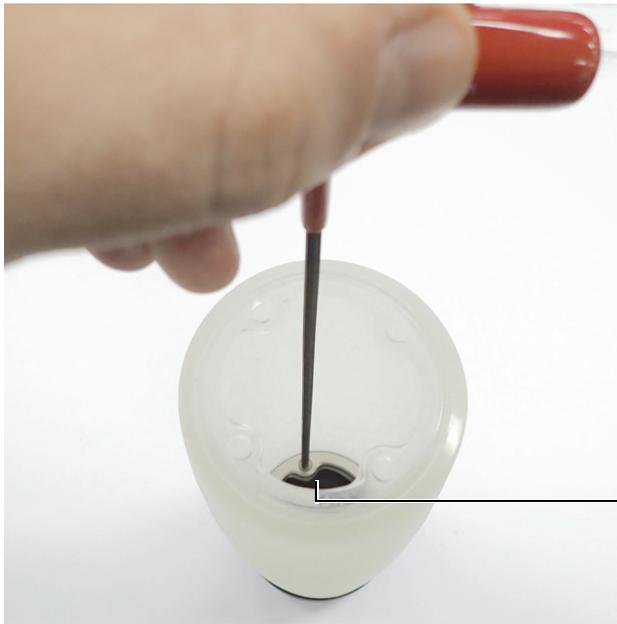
Entfernen des Flachflanschs der Akustikrolle
